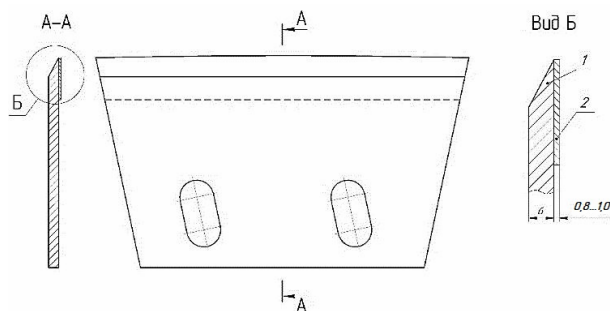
Упрочненный нож измельчающего аппарата кормоуборочного комбайна:
